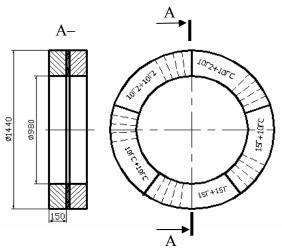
Схема расположения участков сварного соединения, выполненного различными сварочными проволоками
